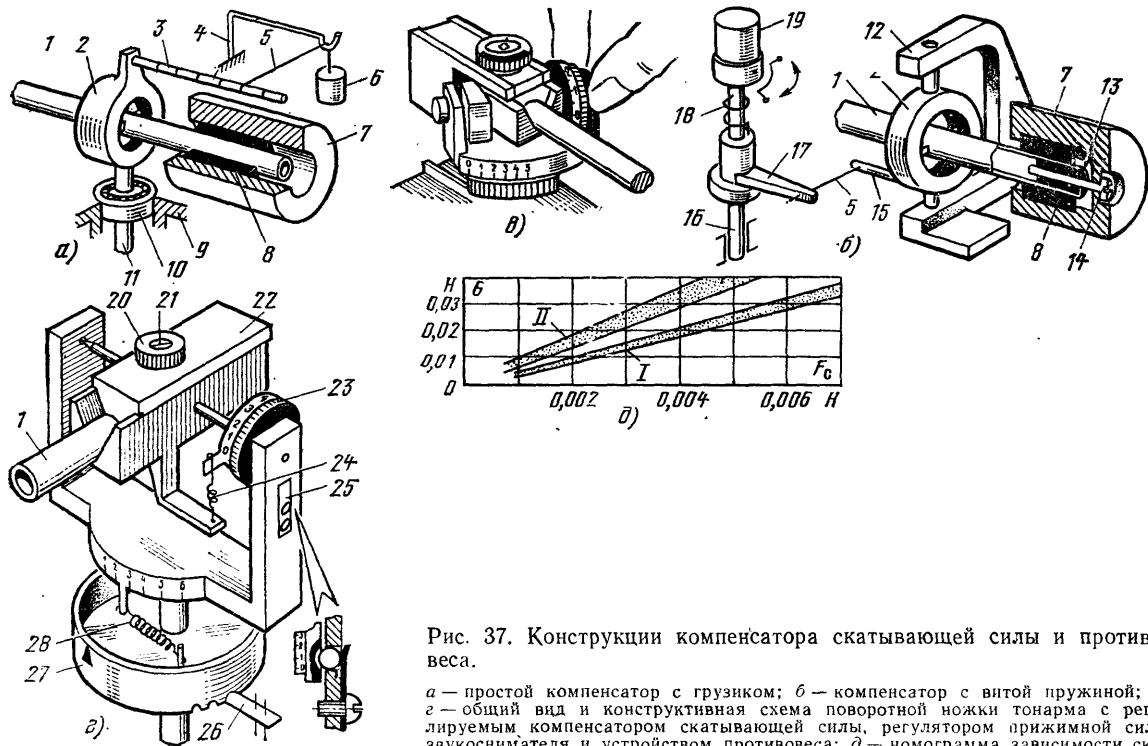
Конструкции компенсатора скатывающей силы и противовеса.
